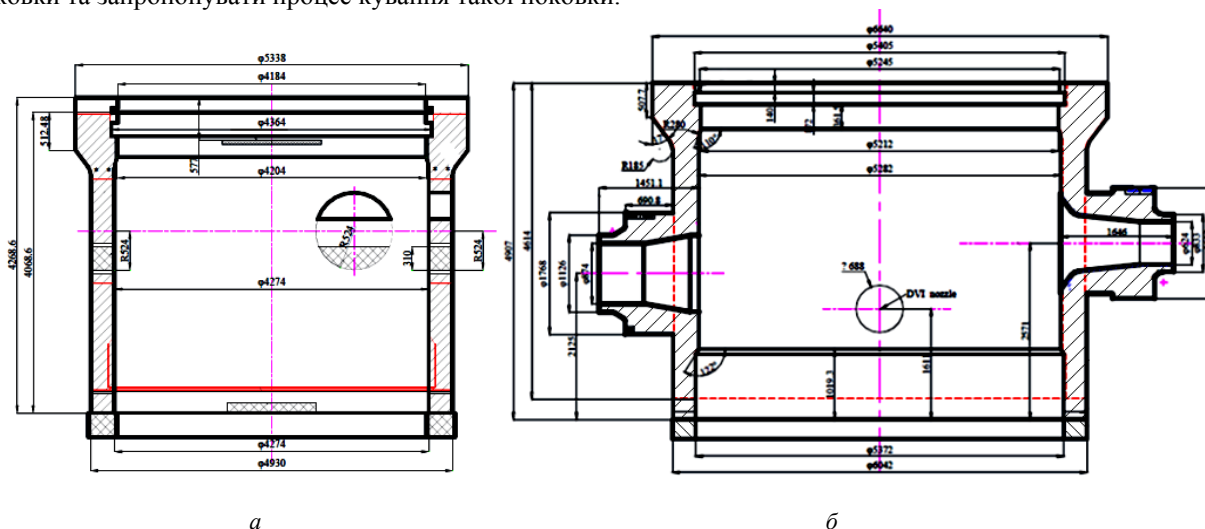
Ескізи обичайок для реактора САР1400: а – з фланцем; б – з фланцем та патрубками
